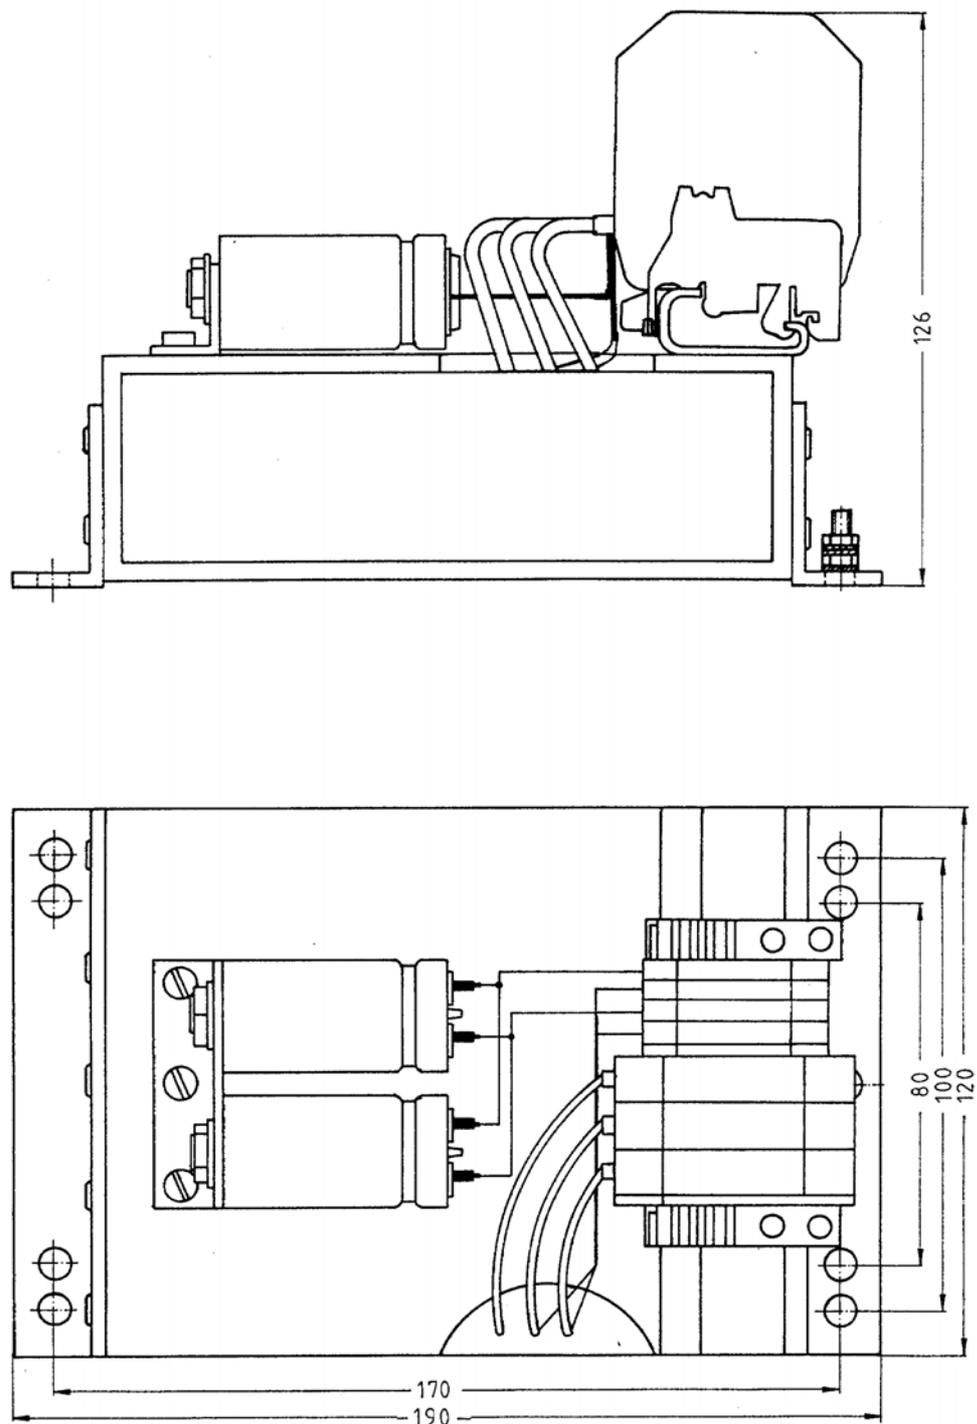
Ansichten Ankoppelgerät AGH502S; Front, Seite
